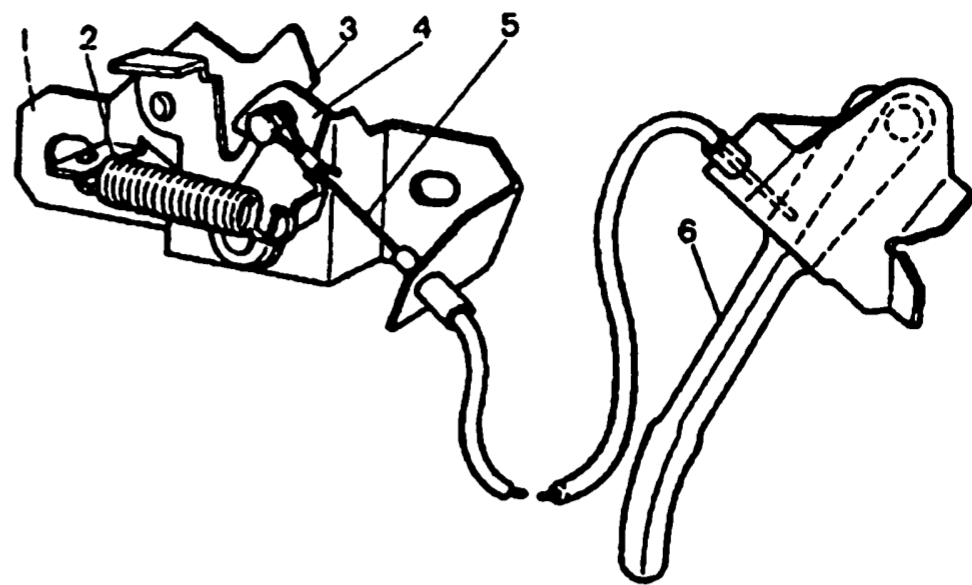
Замок капота: 1 - корпус замка; 2 - пружина; 3 - выталкиватель; 4 - крючок; 5 - трос; 6 - рукоятка привода
